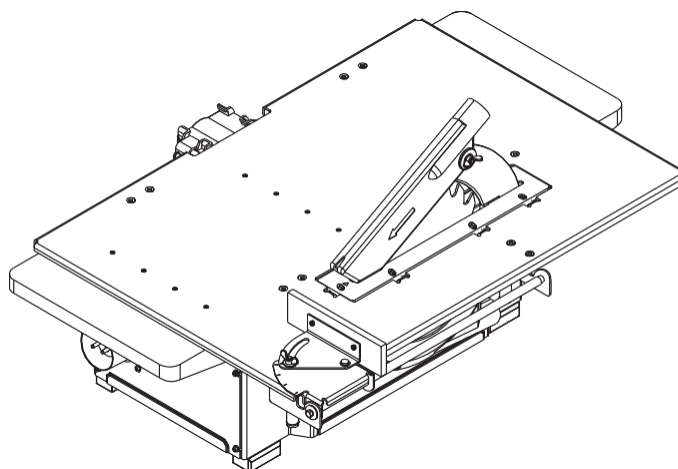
Приспособление для поперечной распиловки под углом 0000-04.
